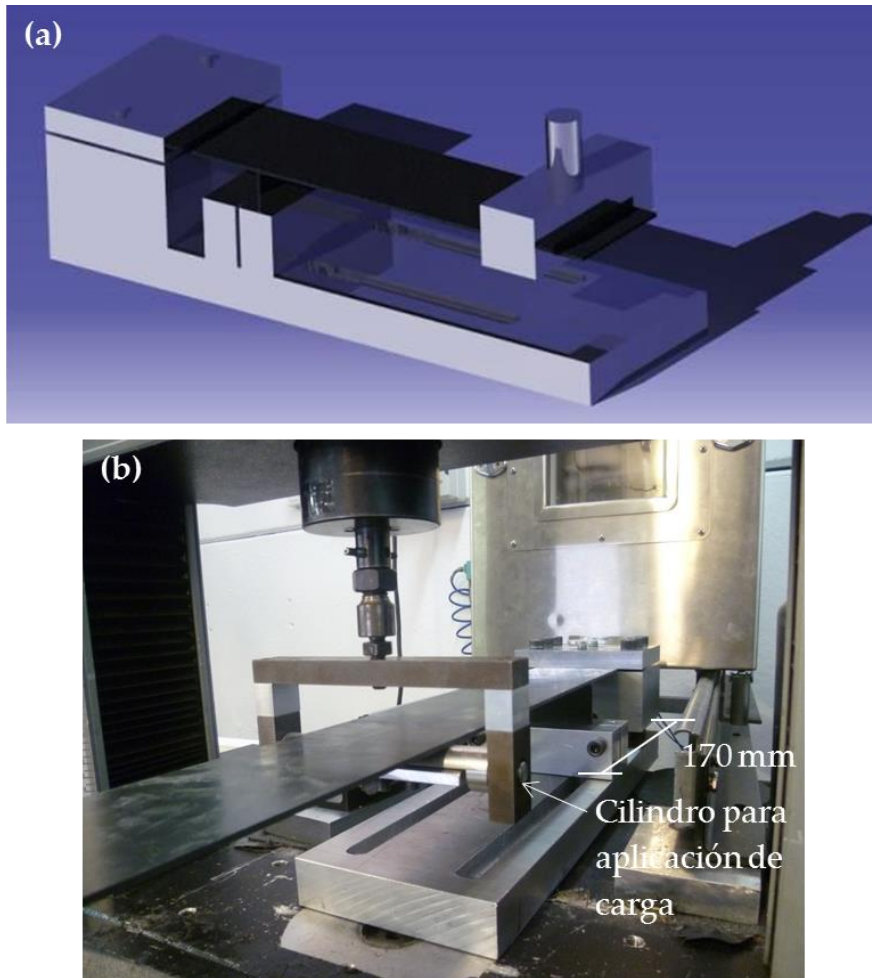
(a) Diseño utillaje empleado y (b) útil fabricado para ensayo estático.
